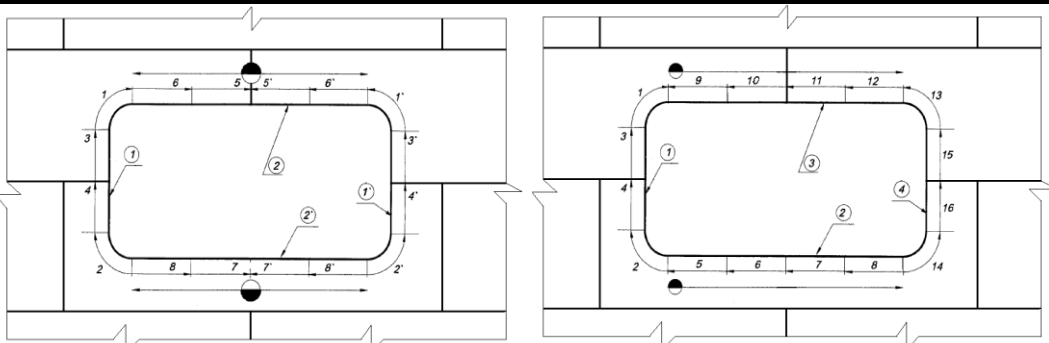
Порядок сварки и конструктивные элементы шва
